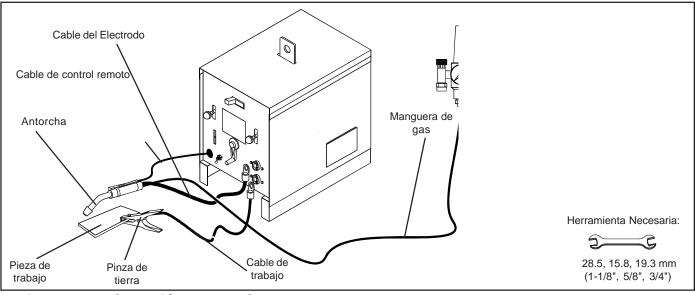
Conexiónes para Soldadura por Proceso con Electrodo de TungstenoTIG.
